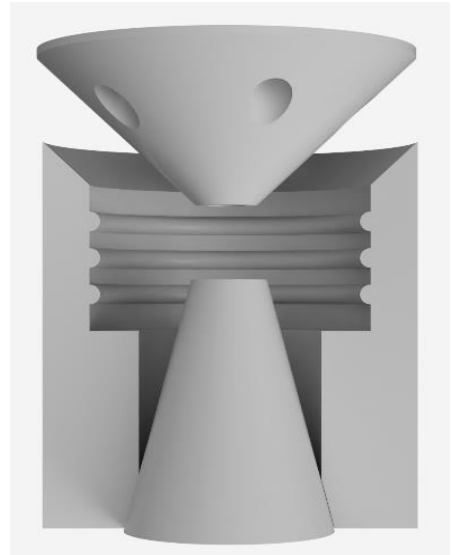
Rendu du prototype de moule pour une tuyère - photo personnelle.
